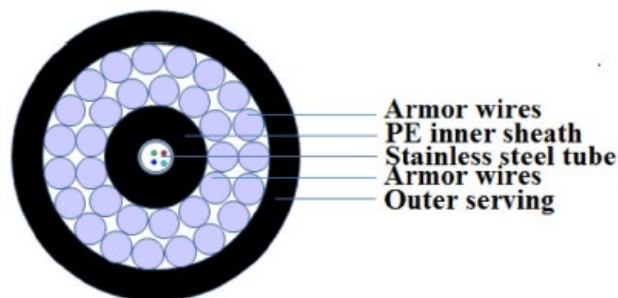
Cavo FOC - Sezione trasversale (Tipico)
